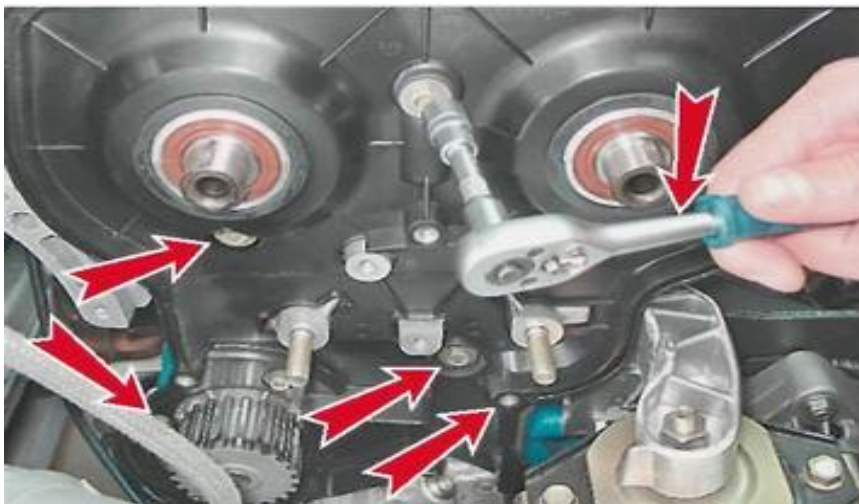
Расположение болтов крепления задней крышки ГРМ
